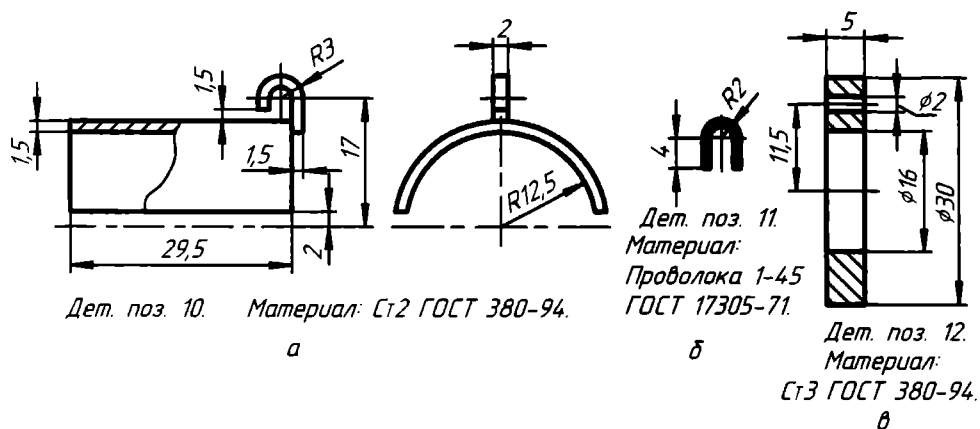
Чертежи деталей защиты: а — щитка; б — скобы; в — шайбы
